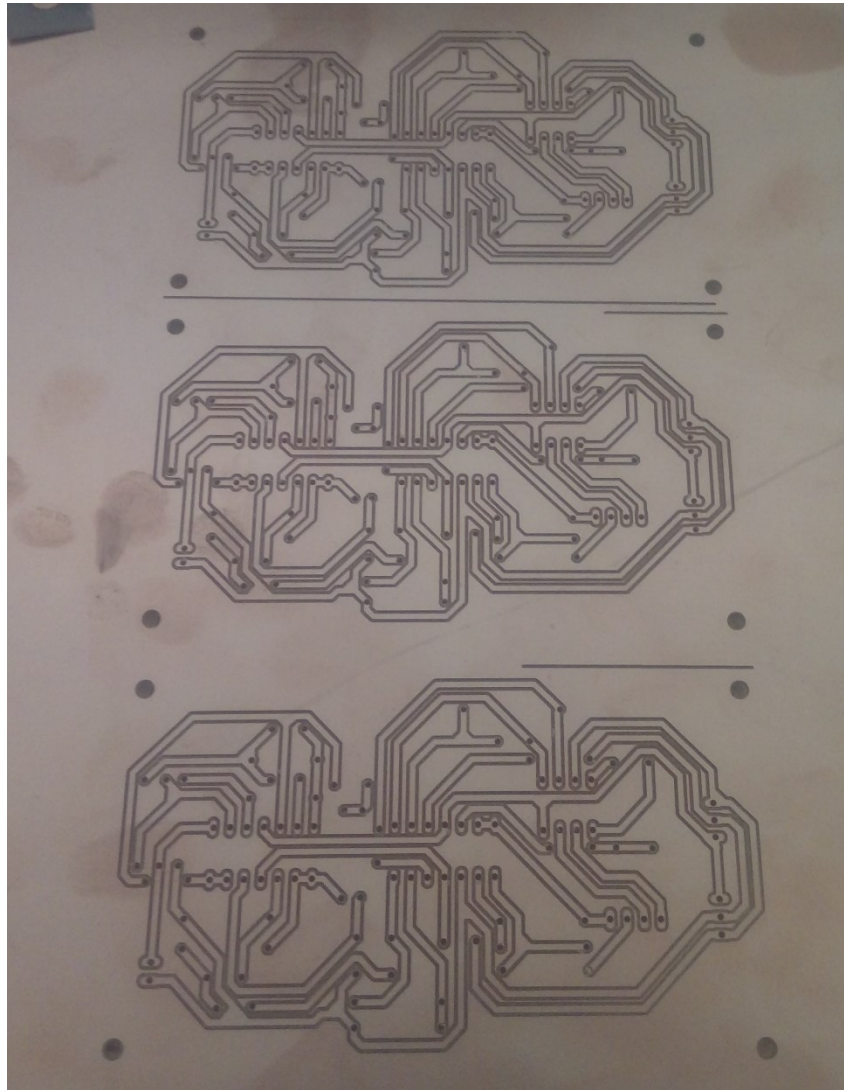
Conjunto de placas PCB ya ruteadas y listas para ser cortadas.
